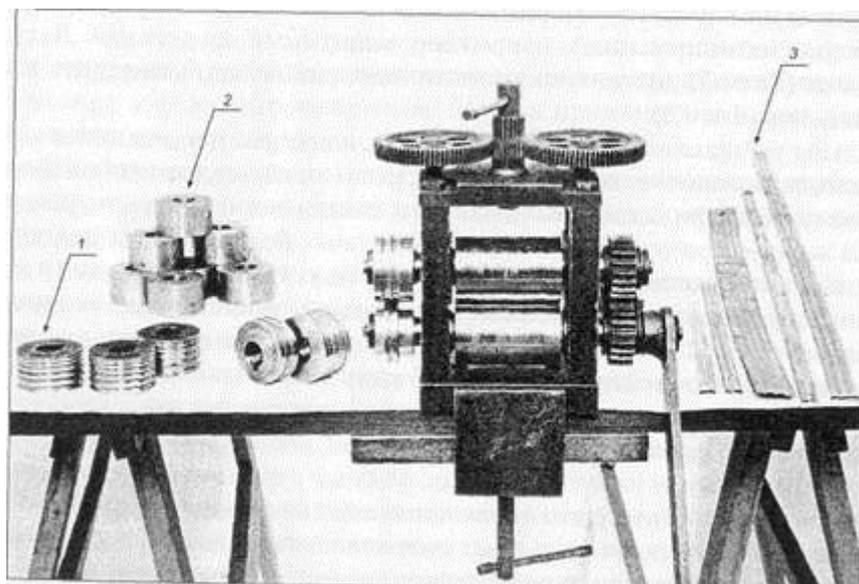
Вальцы для изготовления металлических протяжек: 1) фильеры со сменным профилем; 2) болванки для изготовления фильеров с нужным профилем; 3) варианты образцов, изготовленных протяжек
